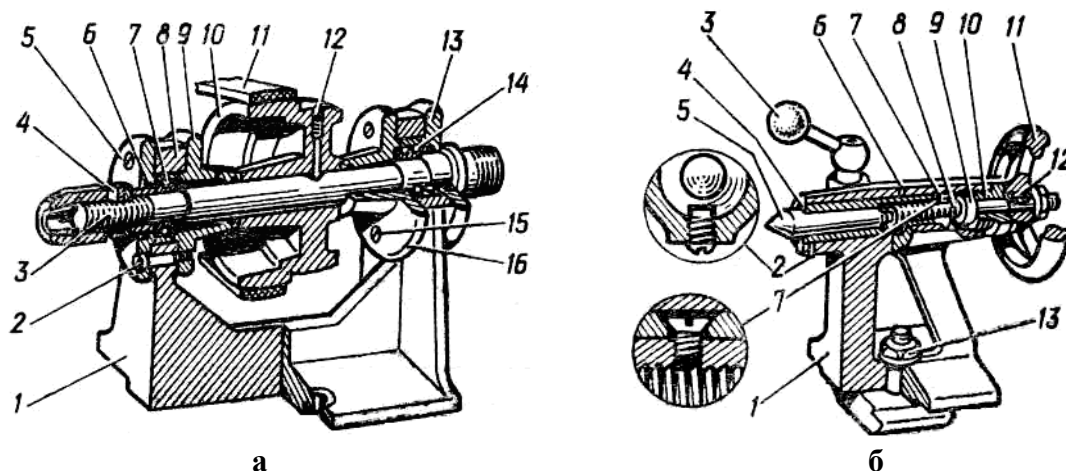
Конструктивні частини токарного верстата для обробки деревини
